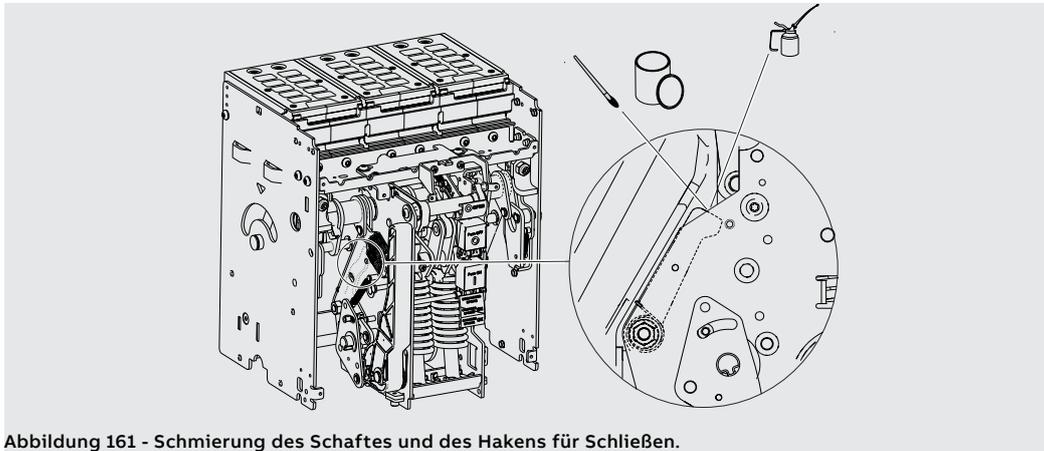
Schmierung des Schafte und des Hakens für Schließen.
